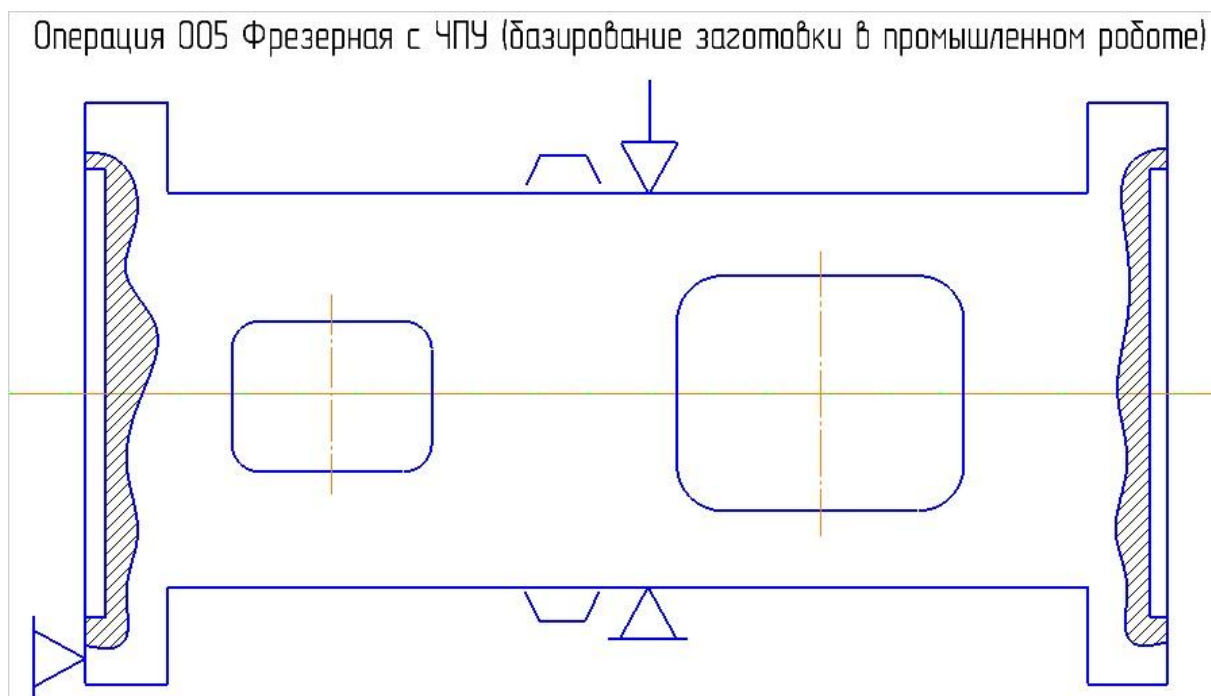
Схема базирования заготовки в промышленном роботе
